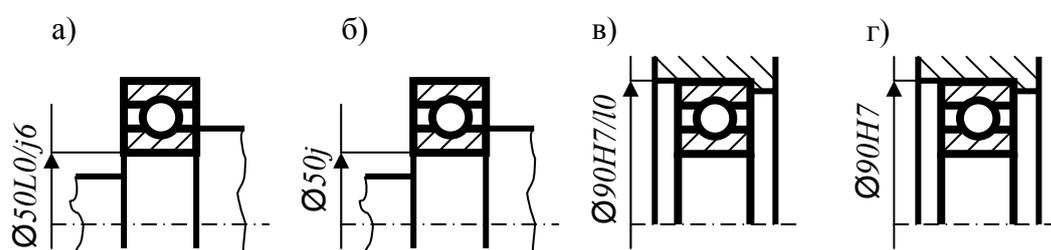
Обозначение посадок подшипников на сборочных чертежах: а,б – на валу; в,г – в корпусе
